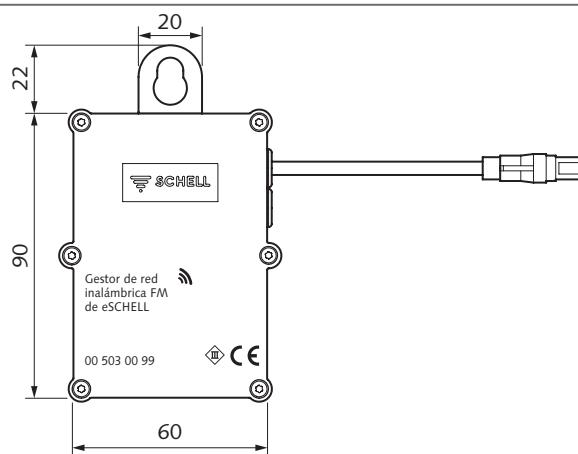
Gestor de red inalámbrica FM de eSCHELL — Dimensiones
